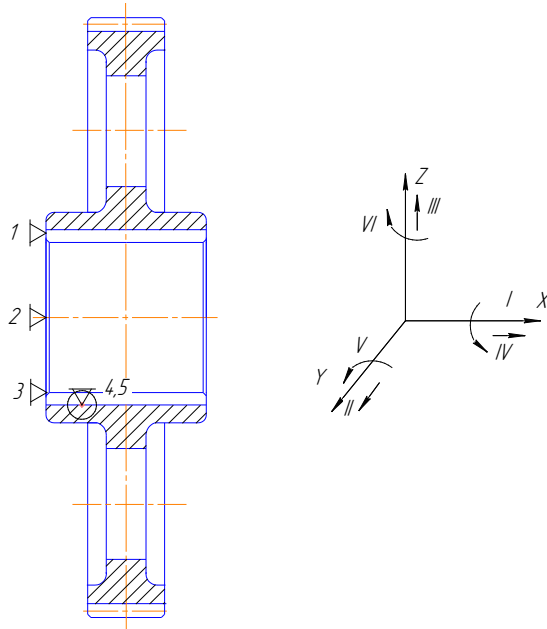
Схема базування зубчастого колеса у вузлі
